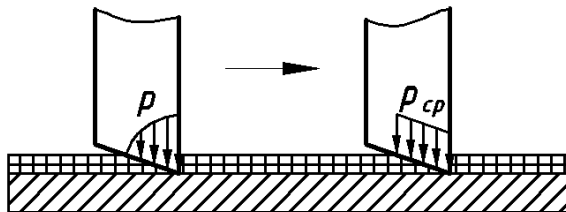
Схема зоны контакта лезвия резца с поверхностью отложений
